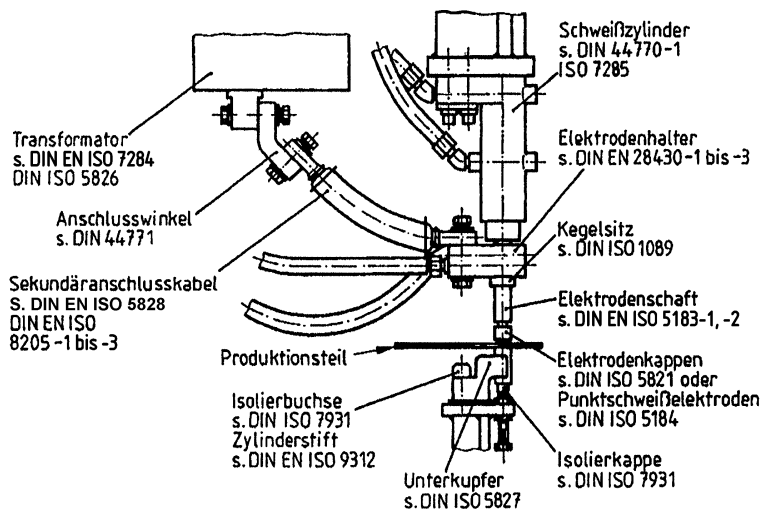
Normen für Widerstandsschweißeinrichtungen
